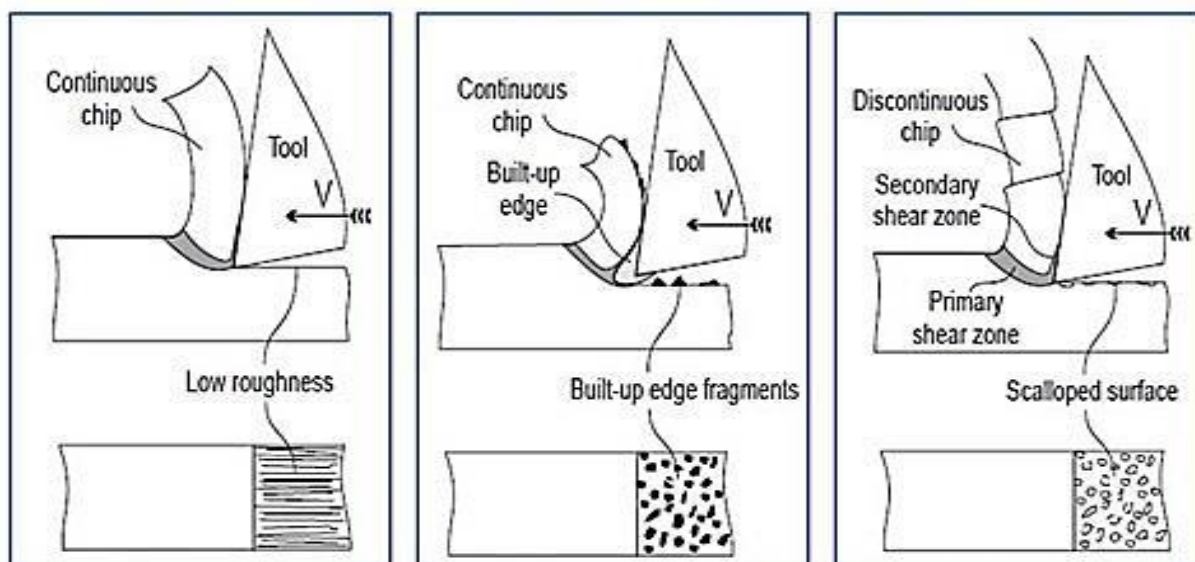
Типы стружек и связь с обрабатываемой поверхностью [28]
